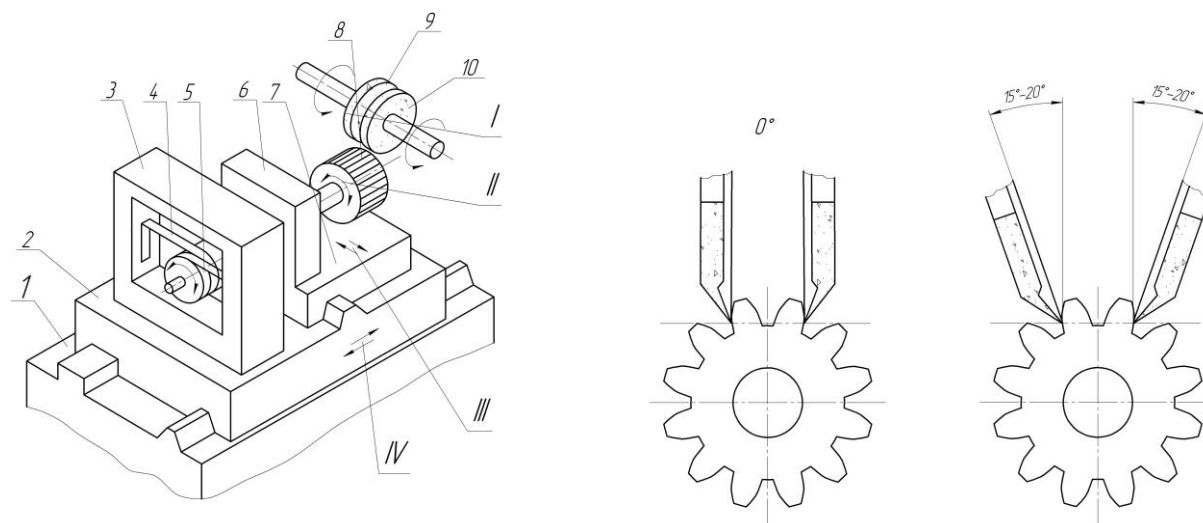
Метод зубошлифования зубчатых колес непрерывной обкаткой двумя тарельчатыми кругами
